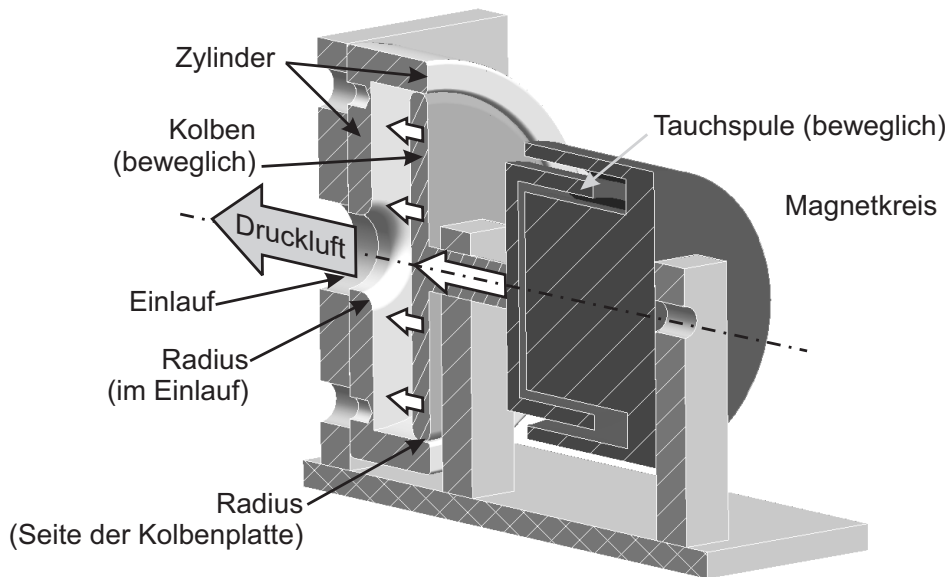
Schnittbild der Baugruppe zur Druckluftherzeugung, bestehend aus Tauchspul-Aktor und Druckzylinder.
